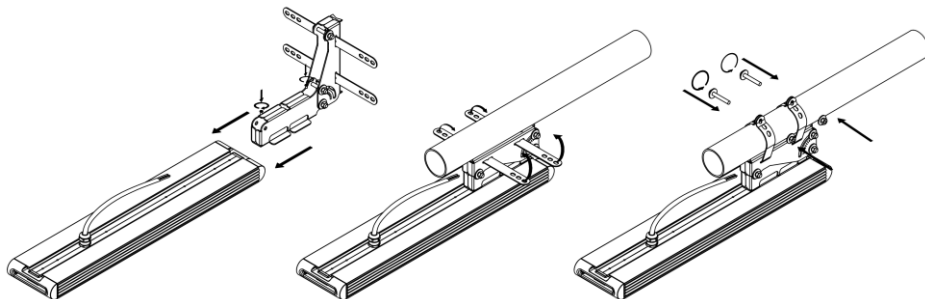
Установка крепления Консоль с регулировкой (на примере Element 0,5x1).
